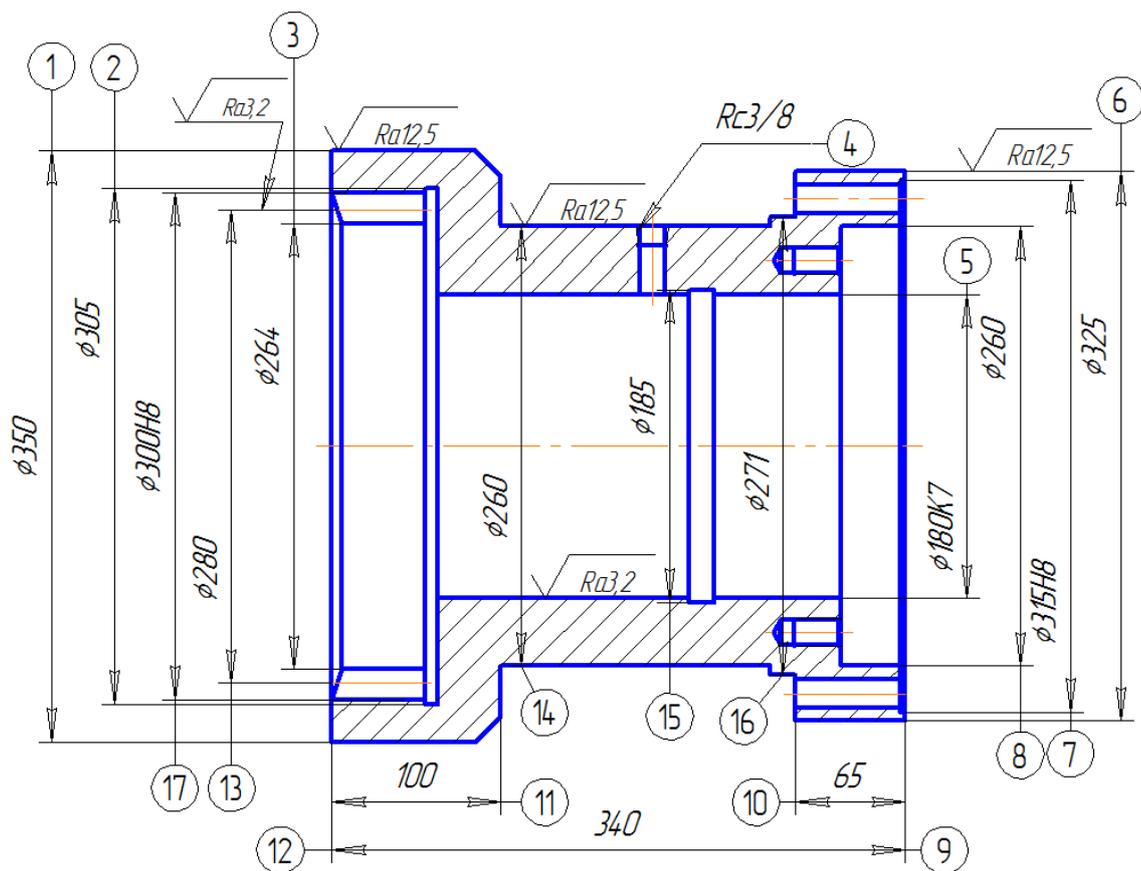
Эскиз детали «Ступица для запасного привода буровой установки»
